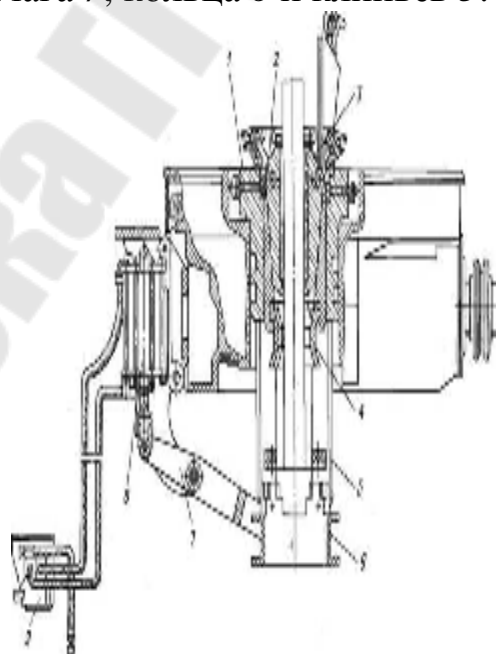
Клиновой пневматический захват: 1 -корпус; 2-вкладыши; 3-клинья; 4- центратор; 5-направляющая планка; 6- кольцо; 7- рычаг; 8- пневмоцилиндр;9-педальный кран
